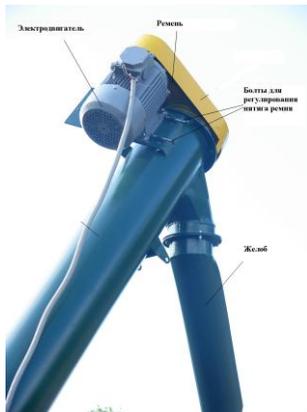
Проверка натяжения ремня разгрузочного транспортеров
